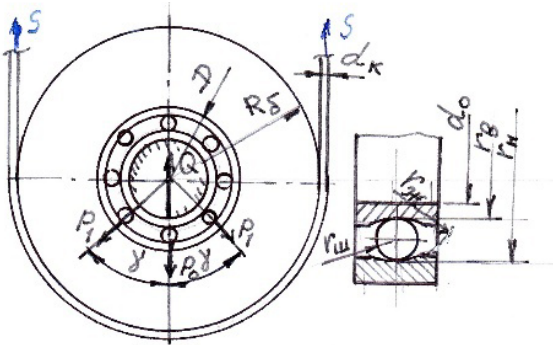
Расчетная схема подшипника блока и принятые обозначения
